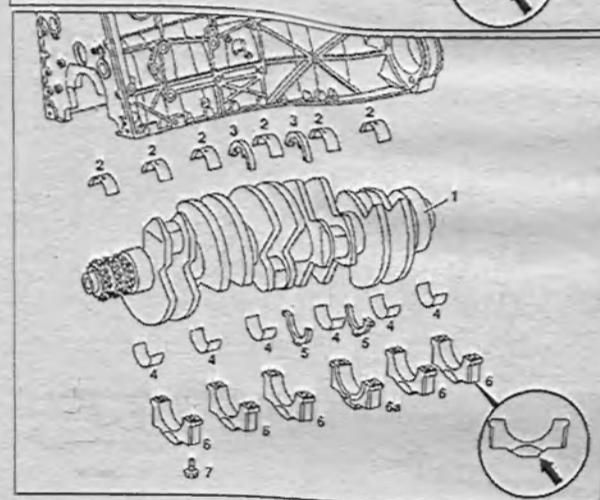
б. Коленчатый вал двигателей OM 612:
